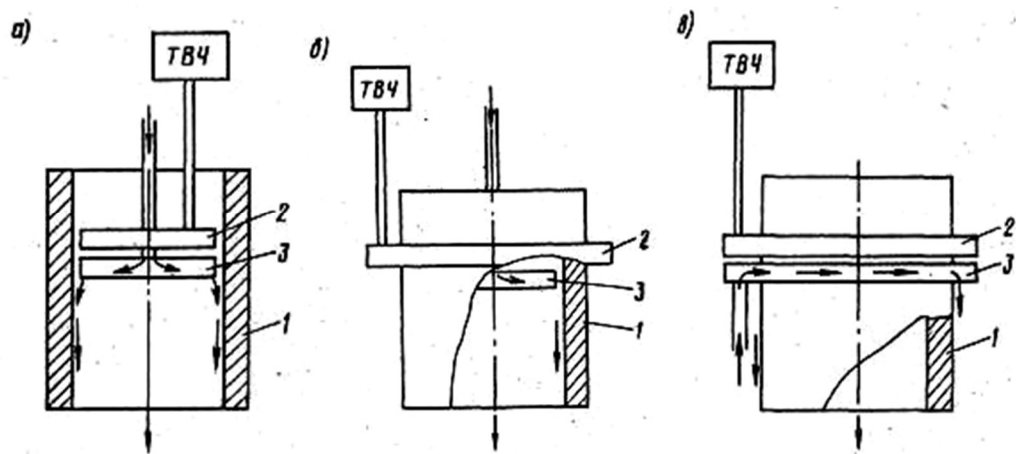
Схема обробки деталі СВЧ [5]:
